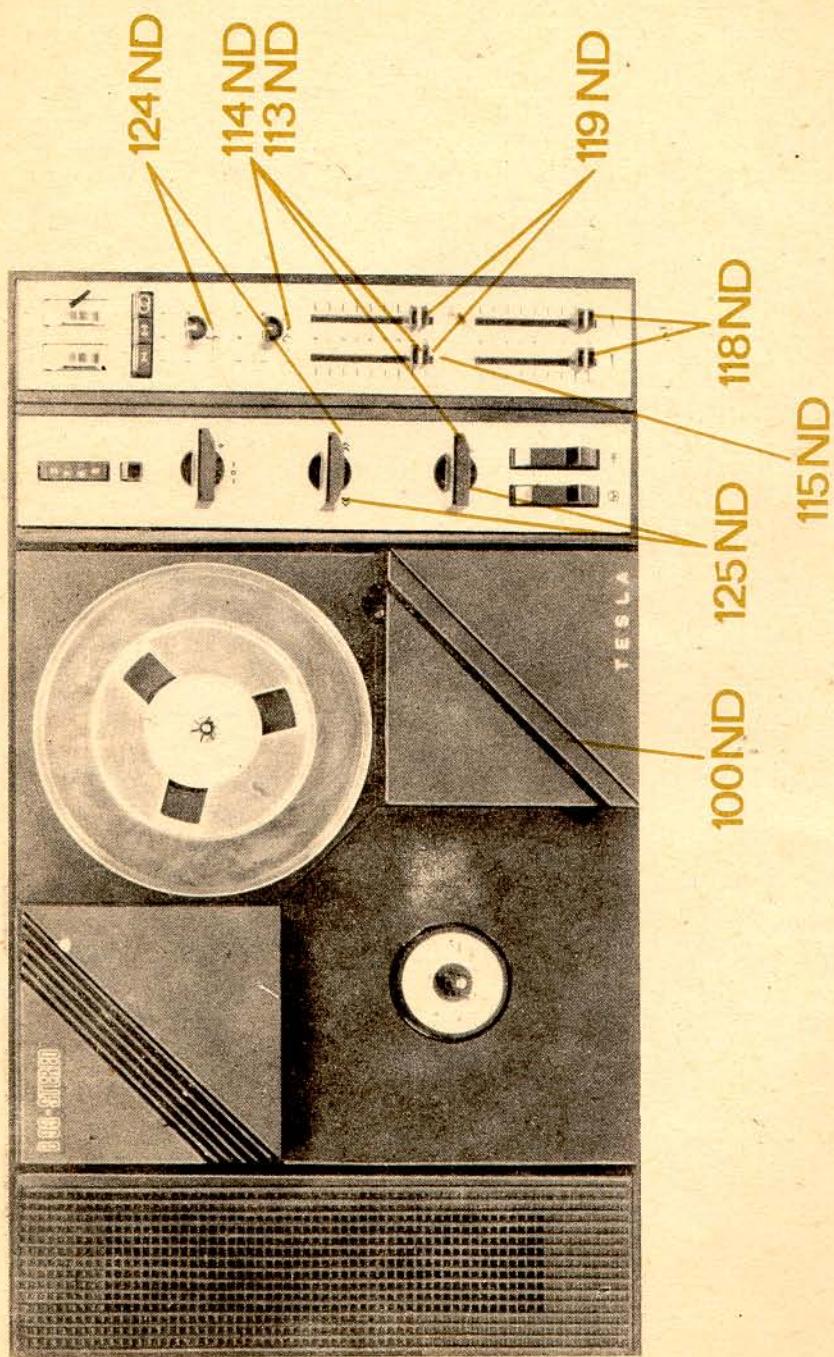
Náhradní díly (vrchní pohled na šasi)
